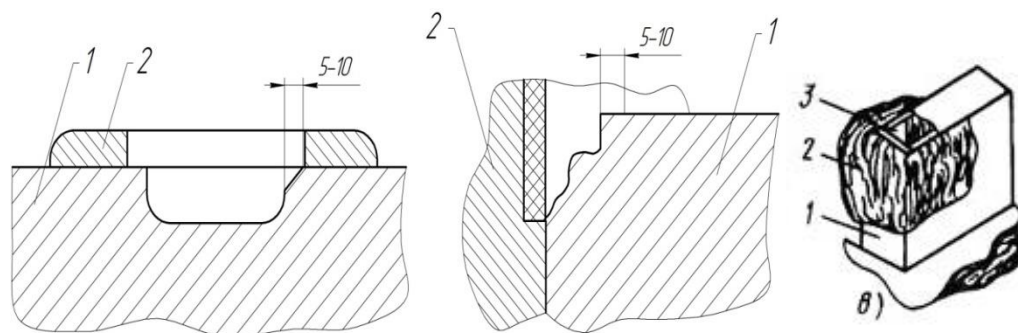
Формовка дефектного місця для гарячого зварювання чавуну
